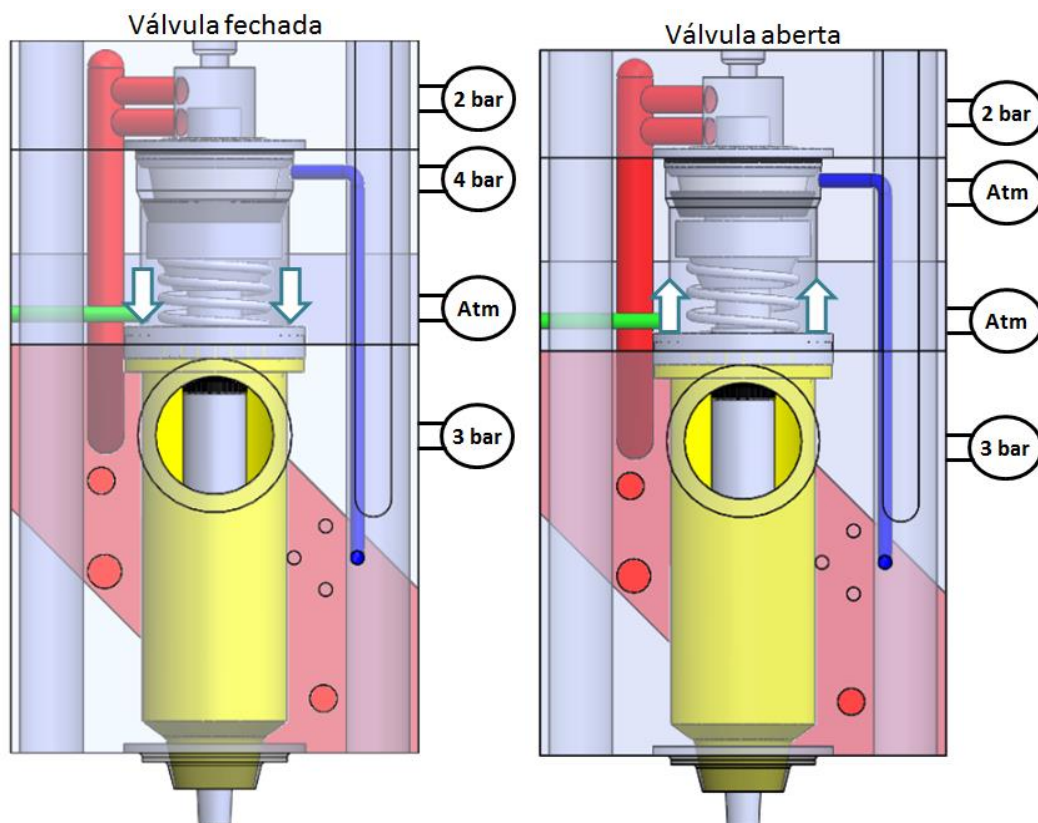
Pressões existentes nas diversas câmaras da válvula de enchimento.
